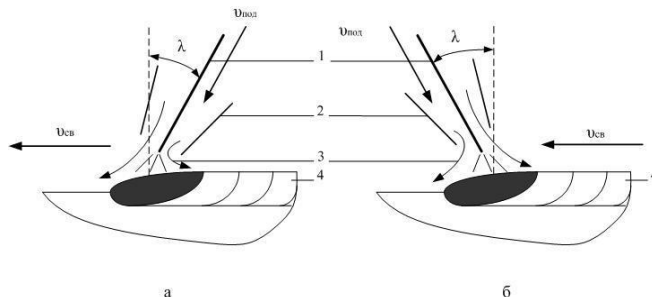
Способы полуавтоматической сварки в углекислом газе: а) углом вперед; б) углом назад; 1-проволока; 2-сопло; 3-защитный газ; 4-сварной шов.
